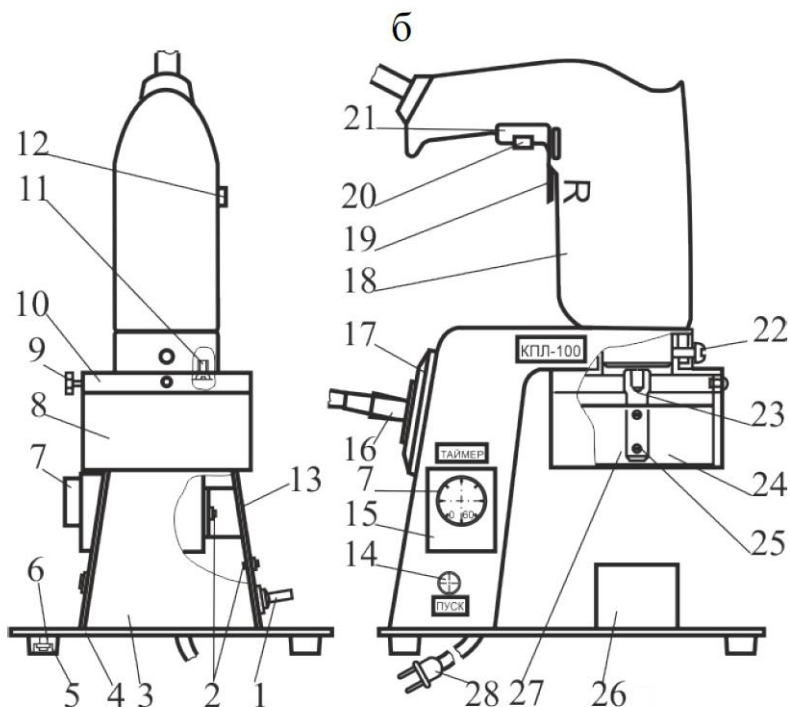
Схема клеверотерки порционной лабораторной КПЛ-100: 1 – тумблер; 2, 6, 9, 11, 22, 23, 25 – винты; 3 – Г-образный корпус; 4 – основание; 5 – ножки резиновые; 7 – штурвал таймера; 8 – терочный стакан; 10 – держатель; 12 – фиксатор кнопки; 13 – крышка; 14 – кнопка пусковая; 15 – таймер; 16 и 28 – вилки кабеля электродрели и сетевого кабеля; 17 – розетка; 18 – электродрель; 19 – переключатель направления вращения (R – правое; L – левое вращение); 20 – колесо регулятора частоты вращения; 21 – переключатель включения/отключения дрели с регулятором частоты вращения; 24 – эластичная лопасть; 26 – мерный стакан; 27 – ротор
